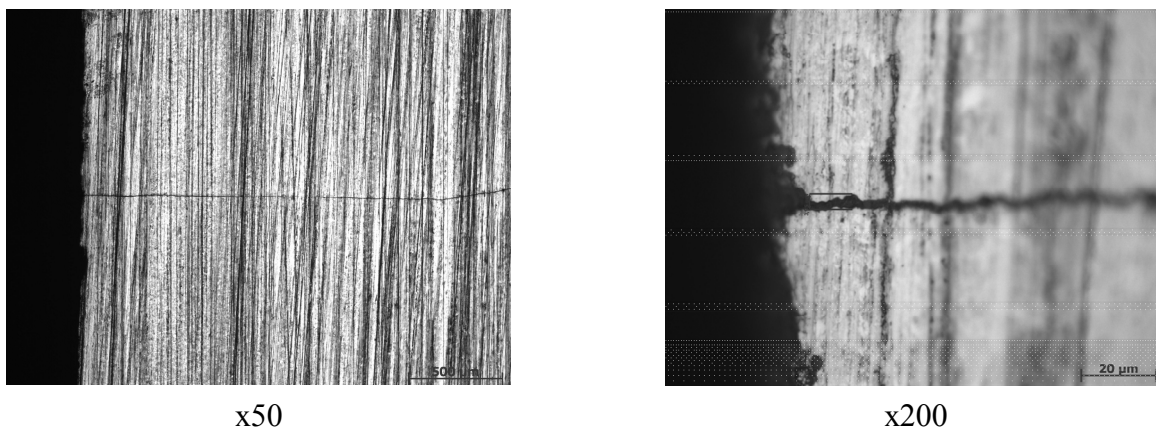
Загальний вид передніх поверхонь твердого сплаву марки ВК8 після заточування колами з карбіду кремнію
